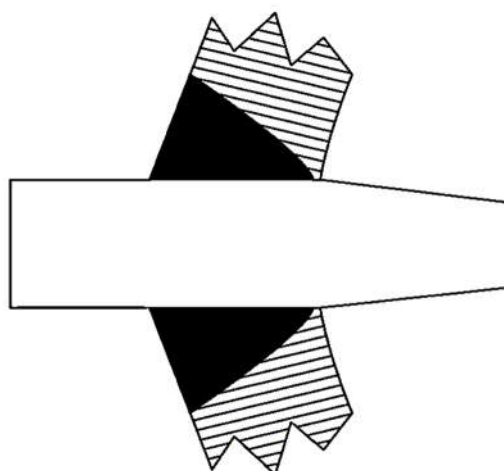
Пример установки гильзы под приварку в стенку трубопровода (Weld-in).
